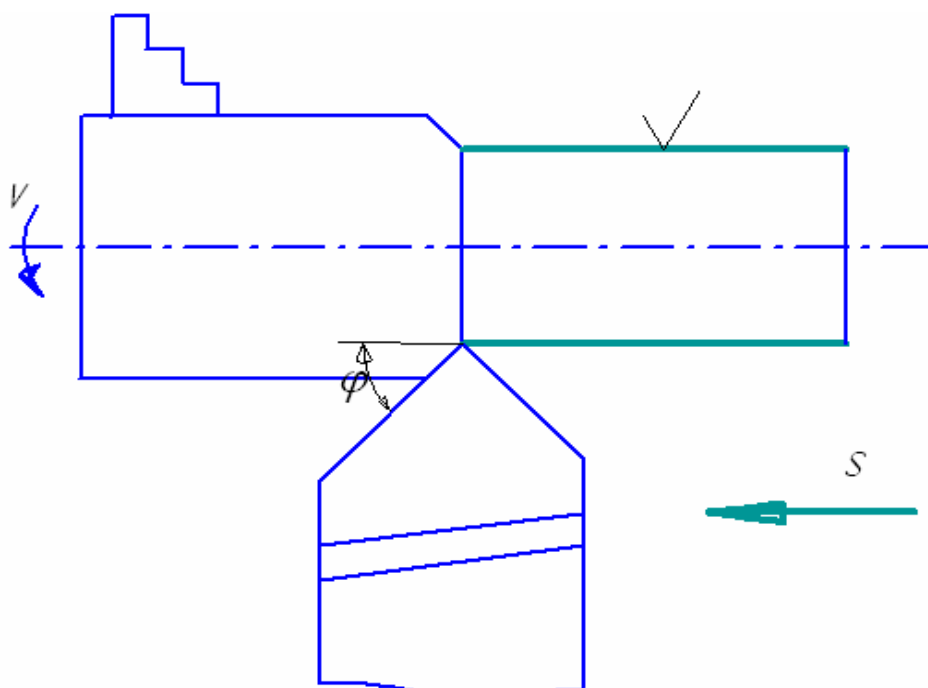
Схема обработки заготовки при определении шероховатости
